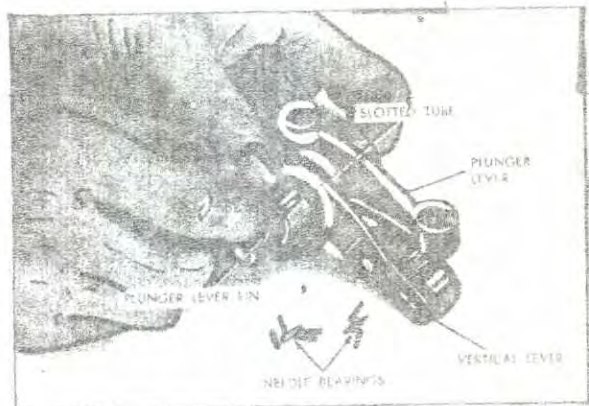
Montaje del pasador de la palanca del émbolo buzo y los cojinetes de agujas.
